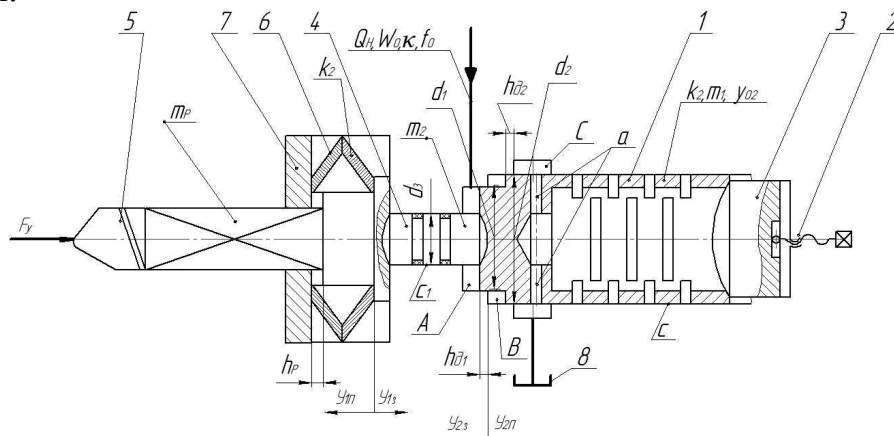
Розрахункова схема гідроімпульсного пристрою для віброточіння
